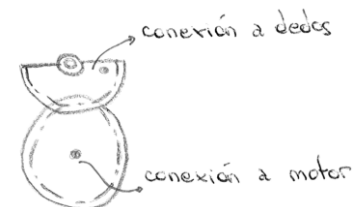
Croquis de mando por engranajes para la transmisión del motor hacia los dedos.
